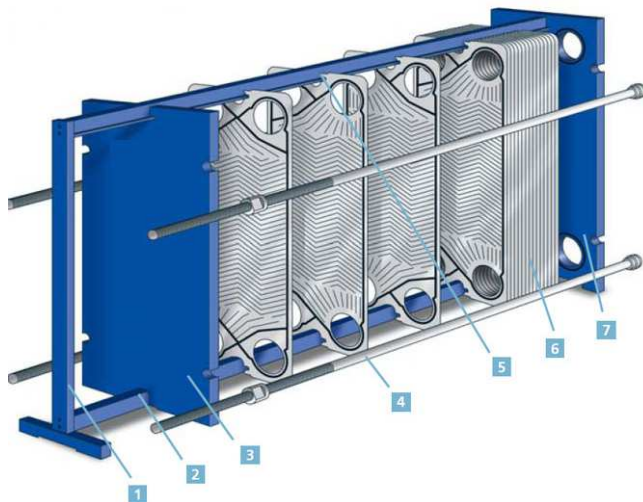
Vue éclatée d'un échangeur à plaques et joints
